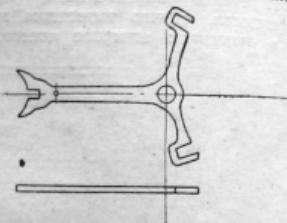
Схема приспособления для второй операции загибы пружинки собачки.
